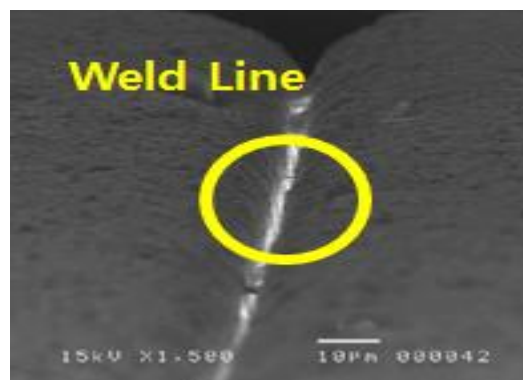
웰드 라인(Weld line) 불량[65].
